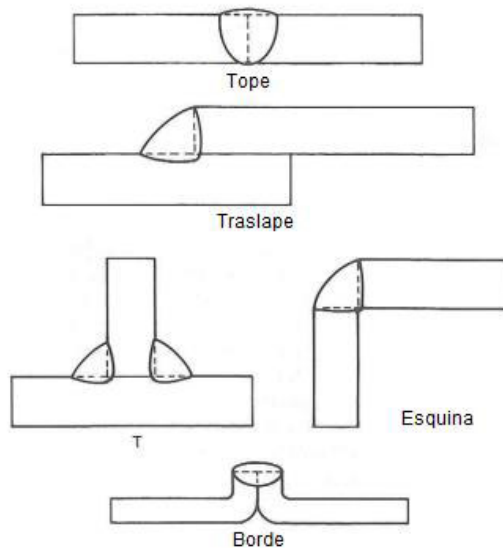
Juntas típicas de soldadura. [10]
